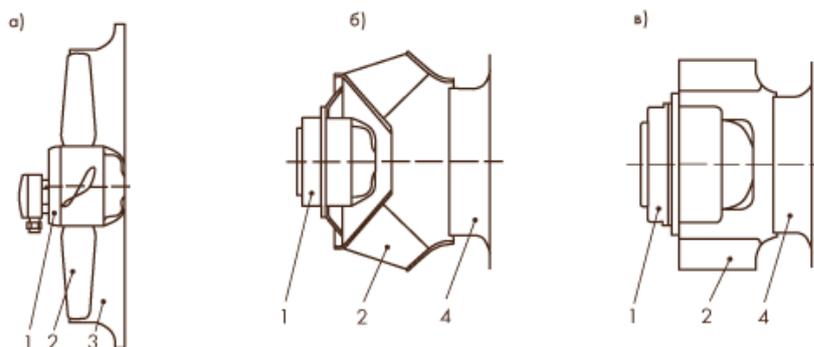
Схемы канальных вентиляторов (а – с осевым, б – с диагональным, в – с радиальным колесами). 1 – двигатель, 2 – рабочее колесо, 3 – обечайка, 4 – коллектор
